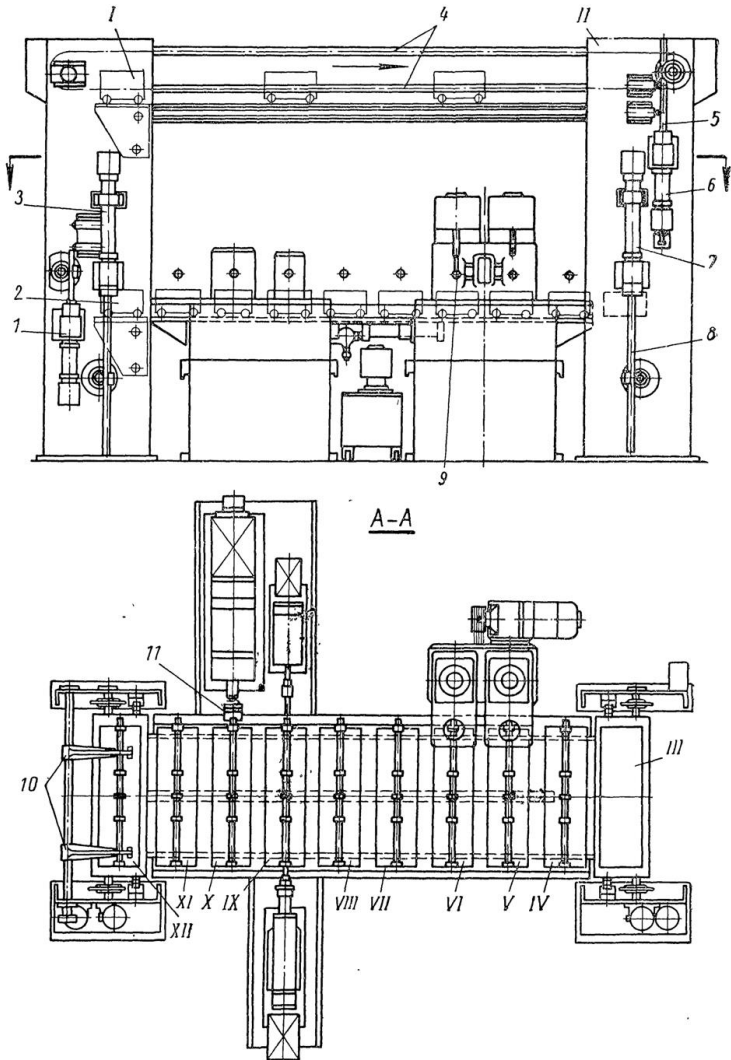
Общий вид автоматической линии для обработки шпоночных пазов и отверстий в распределительном валу
